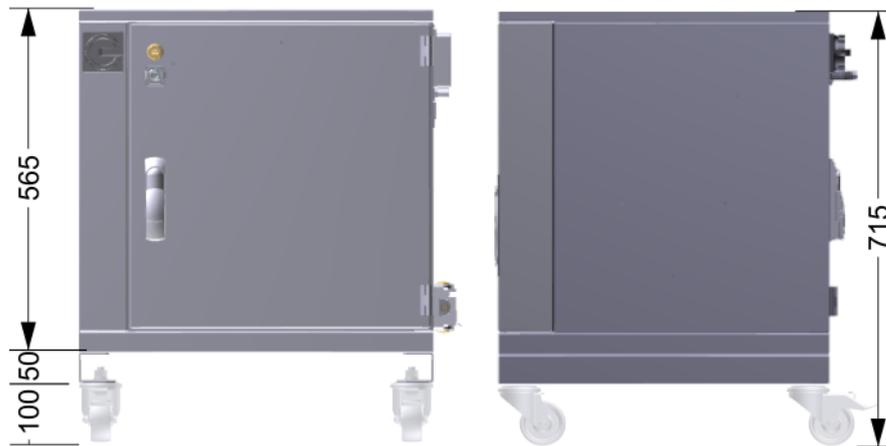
Dimensions avec kit de montage de roulettes (option)
